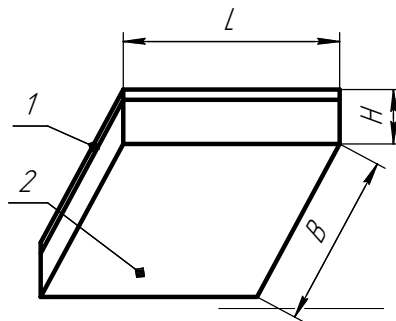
ДПО46-48; 1. Корпус в сборе, 2. Рассеиватель
